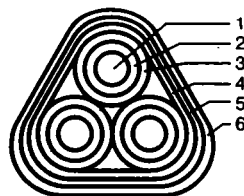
Конструкция силового кабеля марки ОСБ треугольной формы с отдельно освинцованными жилами:
